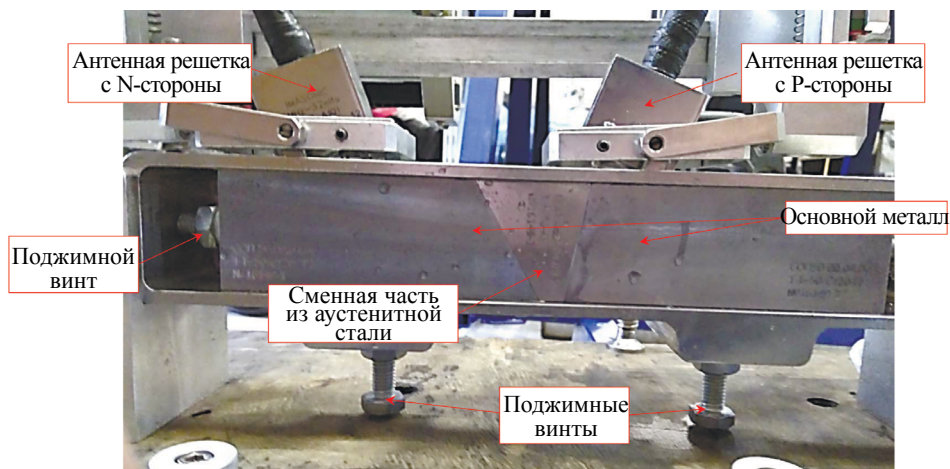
Стенд со сменной частью из аустенитной стали, имитирующей сварное соединение.
